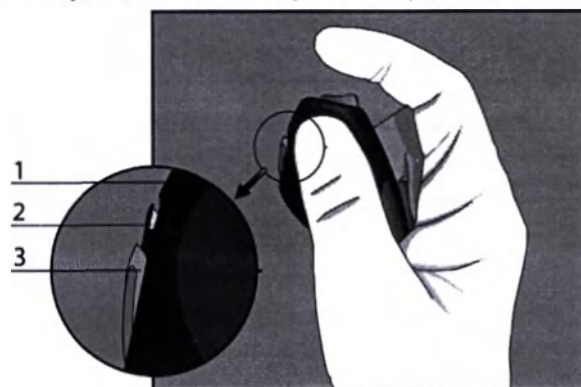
Крепление режущего инструмента, зажимное приспособление не открыто
